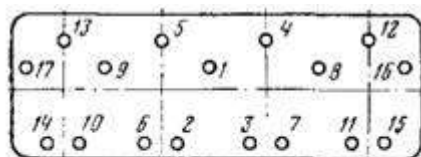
Последовательность затяжки болтов головки цилиндров двигателя ЗИЛ-130
